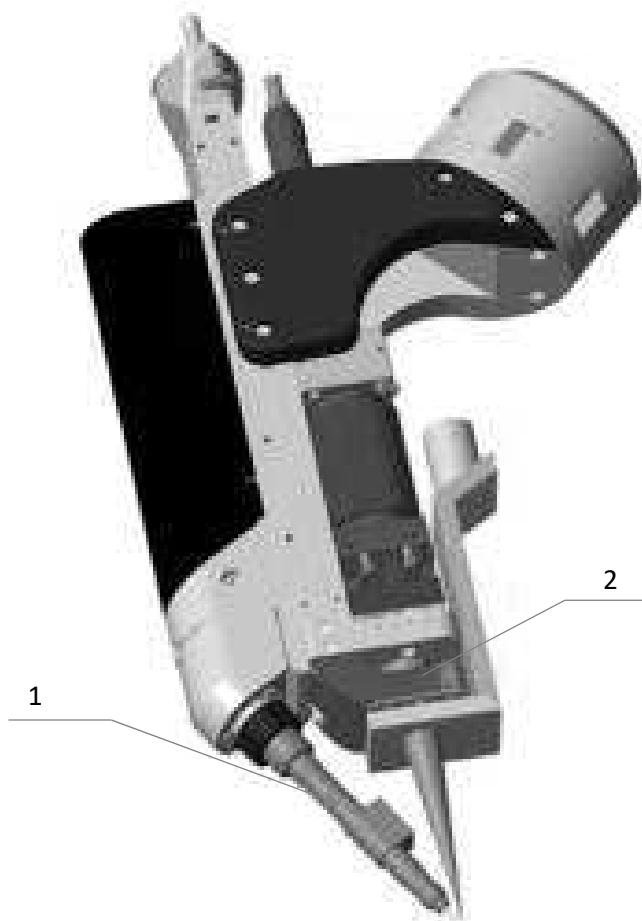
Установка для гибридной лазерно-дуговой сварки
